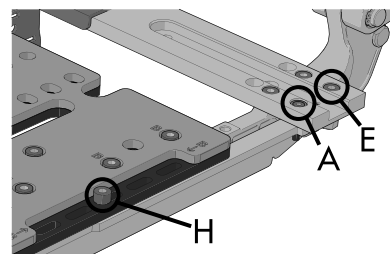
Die vordere Befestigung (H), die M4x20-Schraube (A) mit Buchse und M6x20 (E) mit Unterlegscheibe und Sicherungsmutter an der hinteren Befestigung.
